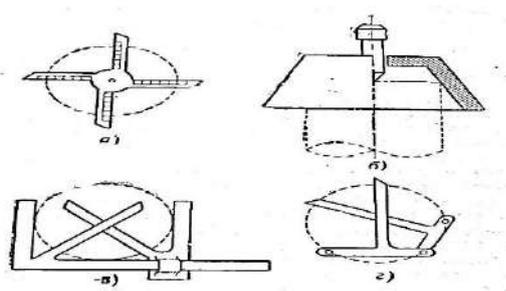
Усовершенствованный центроискатель для центровки цилиндрических болванок
